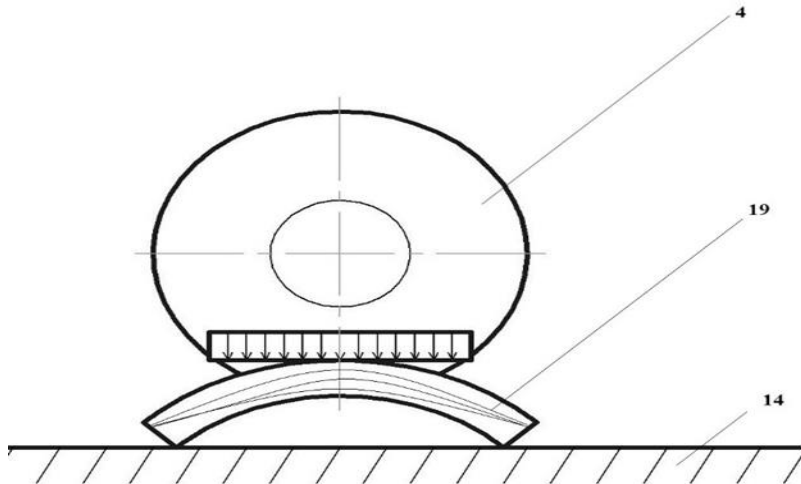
Схема подачи криволинейной заготовки на фуговальном станке
